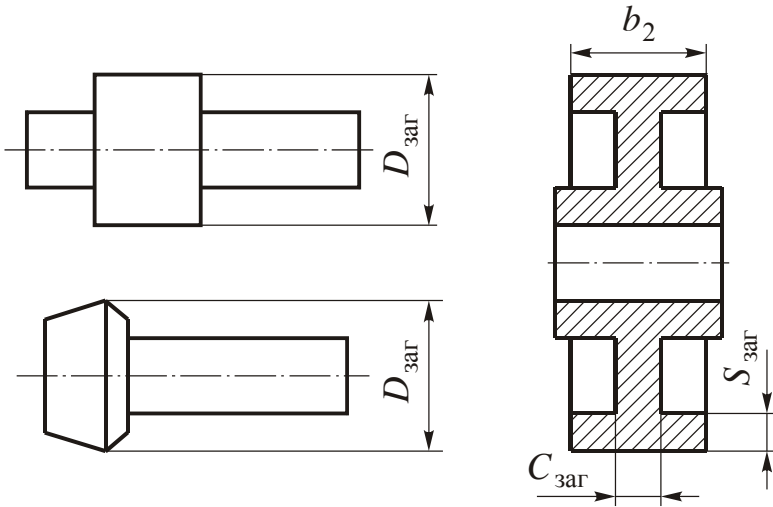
Размеры заготовок (слева – шестерен, справа – колеса)
